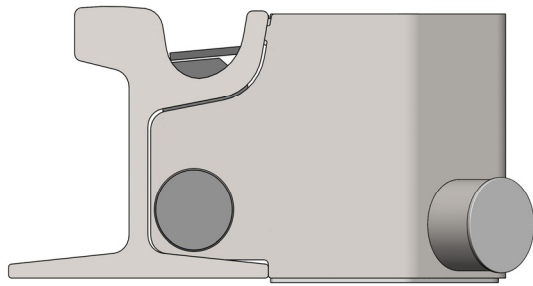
Type SK420-004 (Schienenprofil Ph37a; geschweißt)
